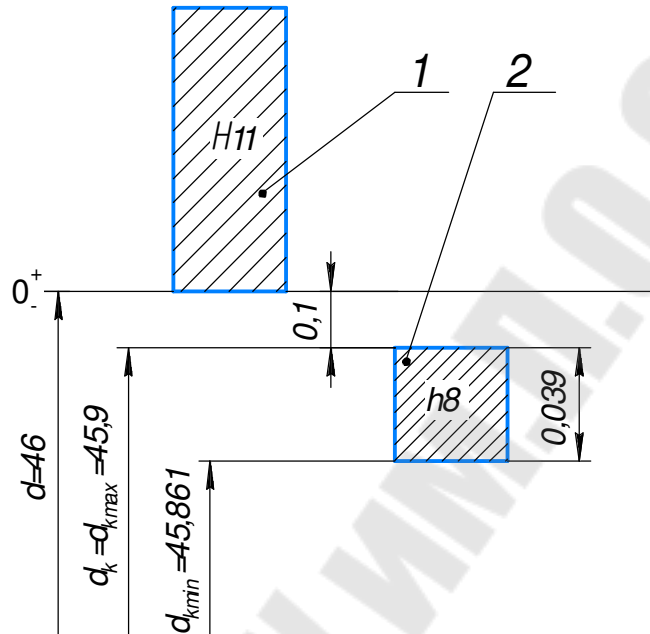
Схема расположения полей допусков, нецентрирующего диаметра d калибра-пробки:
